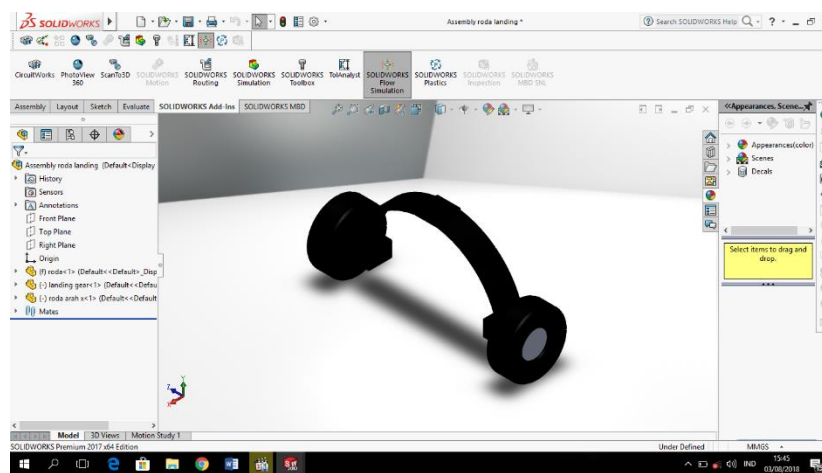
tampak bentuk landing gear setelah menjadi partsolid dan di beri warna.
